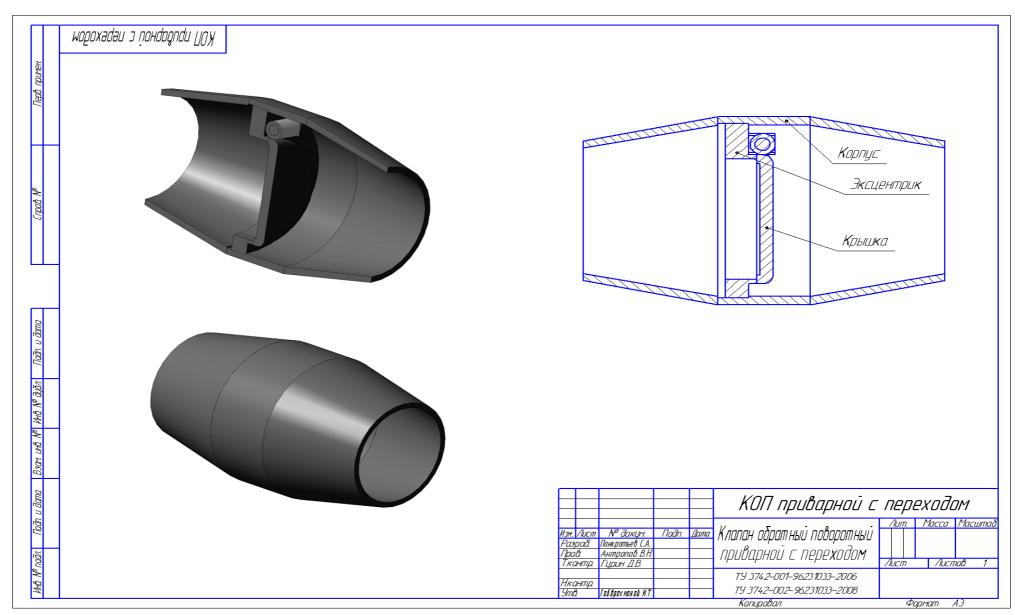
Клапан обратный поворотный приварной с переходом
